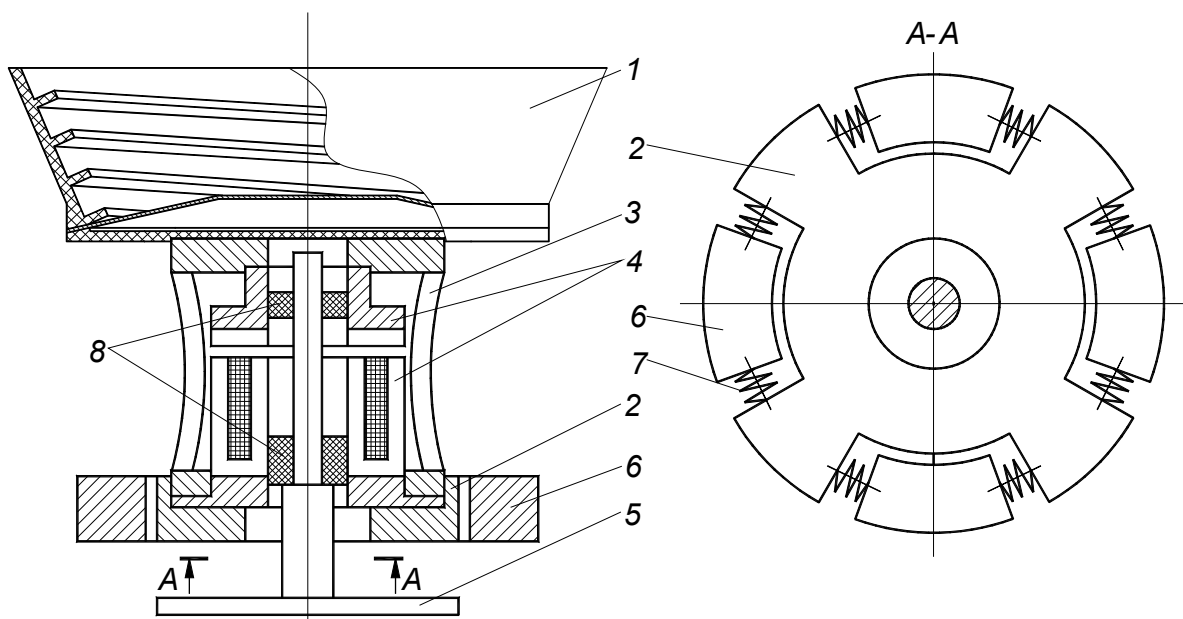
Конструктивна схема вібраційного живильника (варіант з циліндричними пружинами 7)
